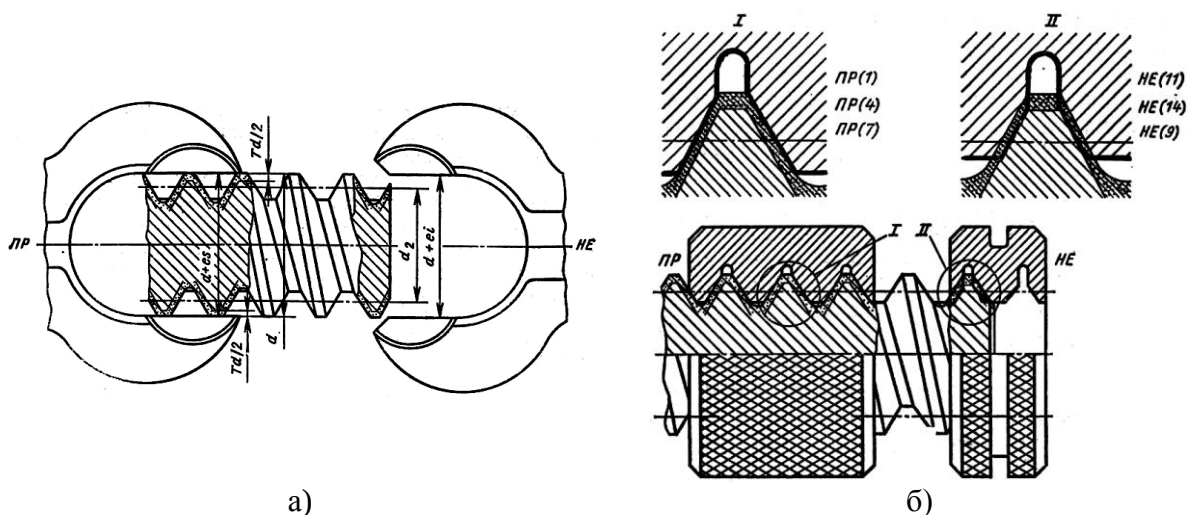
Гладкие калибры-скобы (а) и резьбовые калибры-кольца (б) для контроля наружной резьбы
